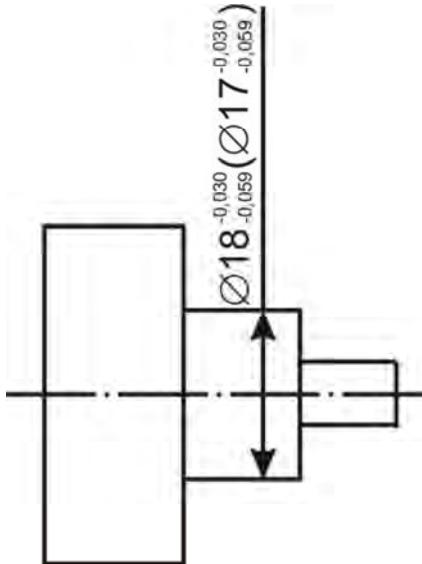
Обозначение допустимых без ремонта размеров и допусков
